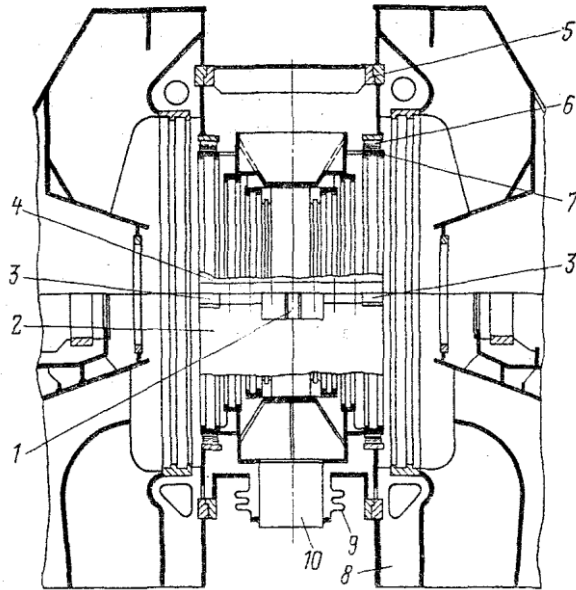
Конструктивна схема двостінного корпуса ЦНТ:
